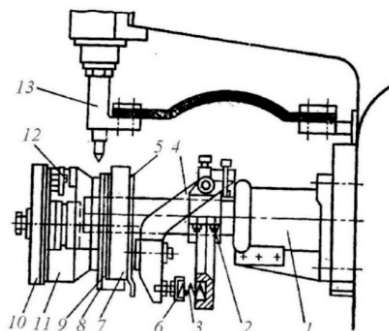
Приспособление для сварки конусных секций, установленное на консоли сварочной машины: 1 – нижняя консоль; 2 – хомут; 3 – пружина; 4 – рычаг; 5, 7 – опорные диски; 6 – опорная шайба; 8 – приспособление для сборки и прихватки; 9 – направляющее кольцо; 10 – съемный диск; 11 – деталь; 12 – фиксаторы; 13 – верхняя головка
